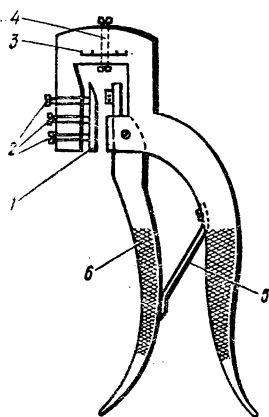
Универсальная разводка: 1 — пластинка; 2 — регулировочные винты; 3 — шкала, показывающая величину развода; 4 — винт с упором, регулирующий высоту отгибаемого зуба; 5 — пружина; 6 — рычаг для отгиба зуба от пилы.
